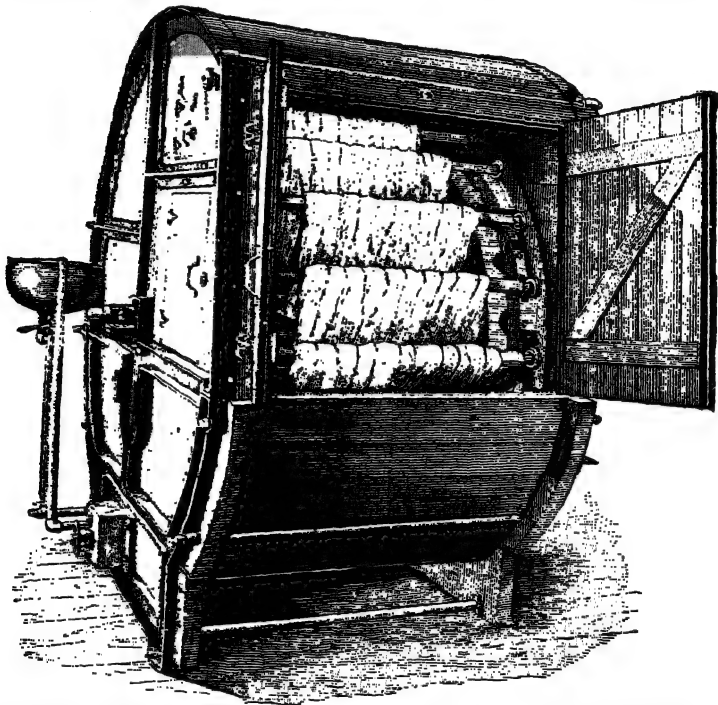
Klauder-Weldon's Garnfärbemaschine. (Aussen-Ansicht.)
